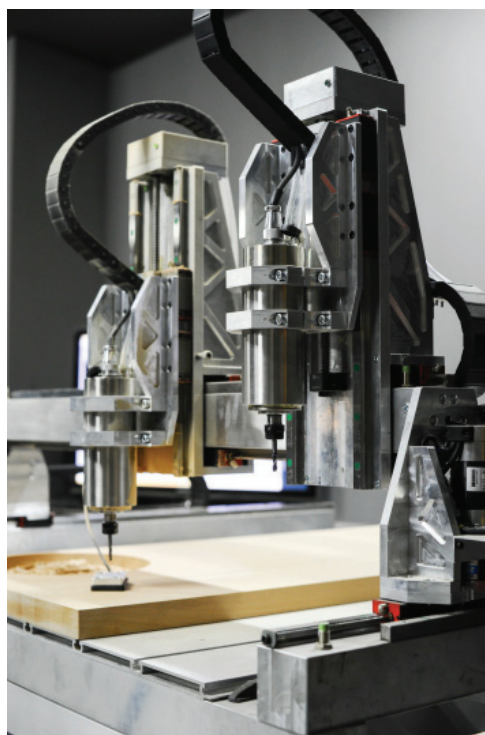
Фотография механической системы фрезерно-гравировального станка с ЧПУ АТС-3000
